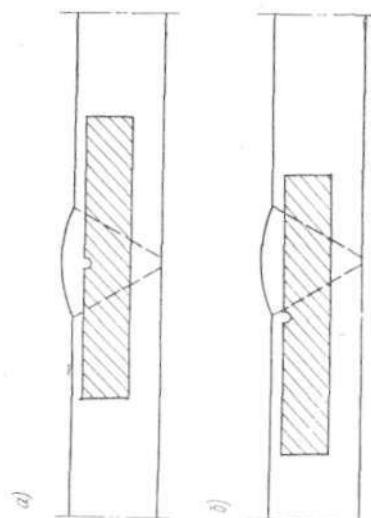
Образцы для испытания на удар: а — металла шва; б — металла переходной зоны.
